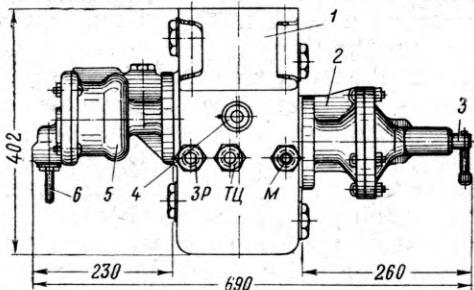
Общий вид воздухораспределителя усл. № 270-005-1:
